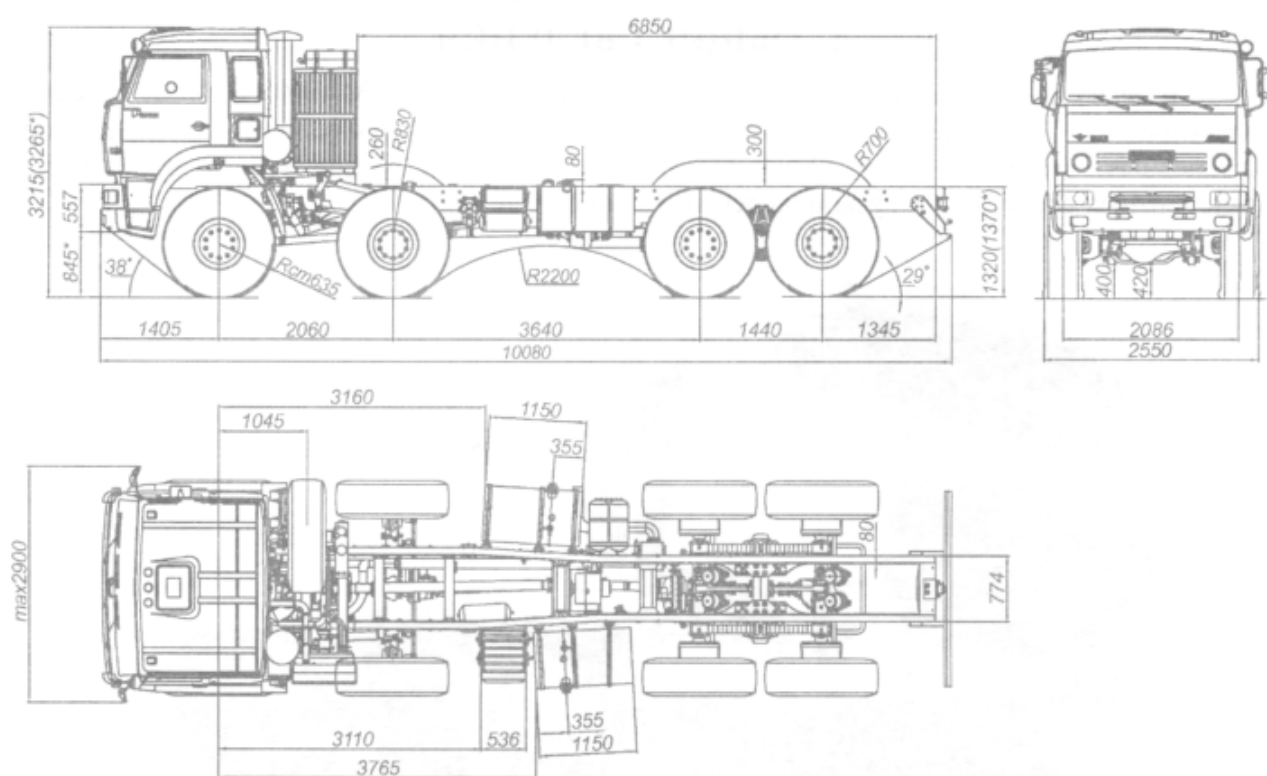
Шасси автомобиля КАМАЗ-6560. Габаритные размеры.
